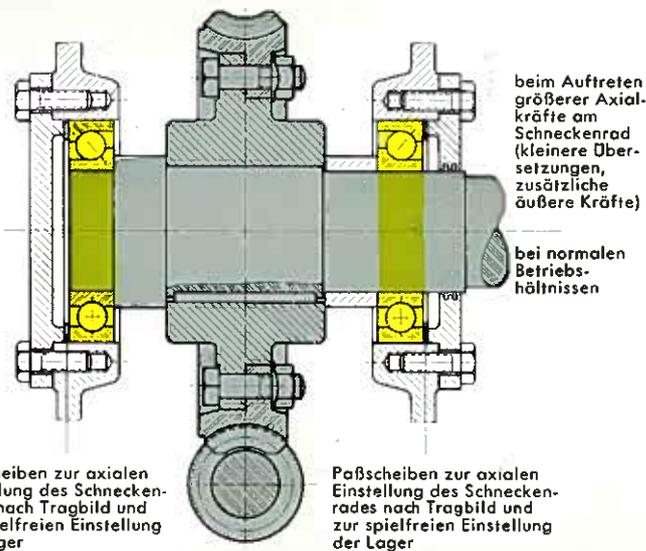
Einbaubeispiel für CAVEX-Schneckenrad
